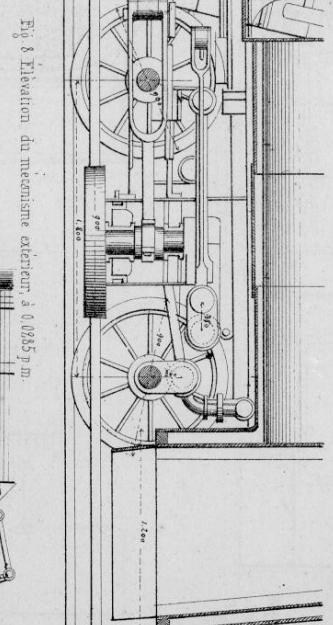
Elevation du mécanisme extérieur à 0.0285 p.m.
